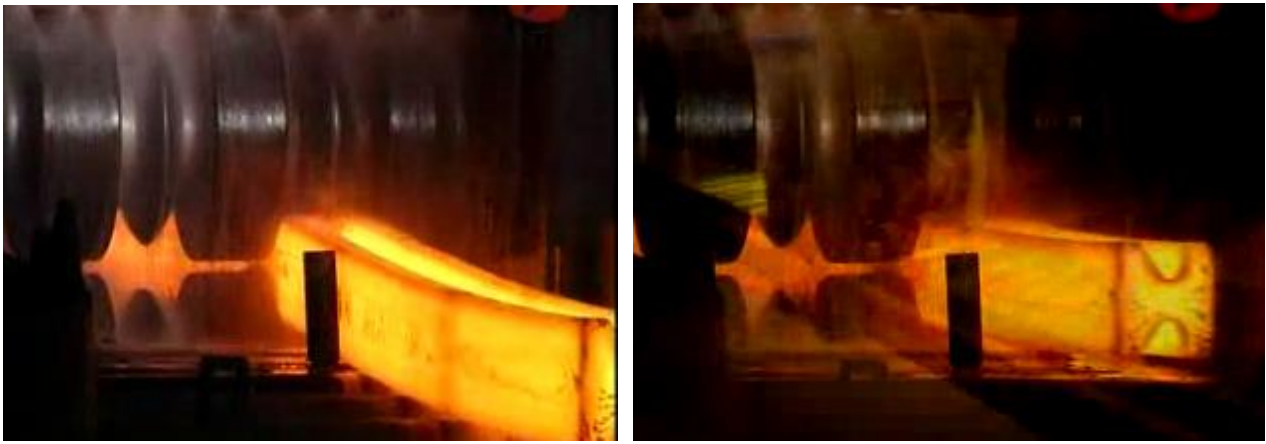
Вид валков первой трехвалковой клетки с разрезными калибрами для прокатки двутавровой балки
